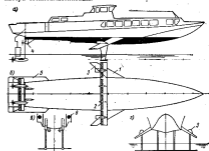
Схема общего вида и крыльевого устройства пассажирского газотурбохода «Тайфун»: а — общий вид; б — схема расположения крыльев (план); в — носовое крыльевое устройство; г — носовое крыльевое устройство; д — шарнир носового крыла; е — носовое крыло; ж — гребная колонка; з — корпус раздвижного станда; 4 — колонка с гребным винтом для вида СПК в подвешенном состоянии; 2 — бортовой режущий для раздвижения газотурбохода; 3 — труба газотурбохода.
